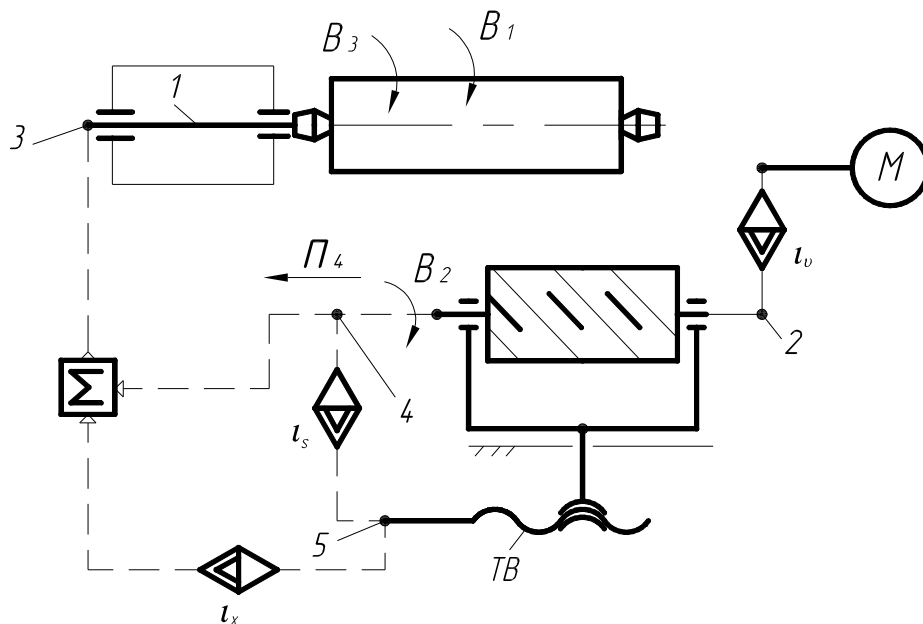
Структурная схема станка для фрезерования резьб червячной фрезой
